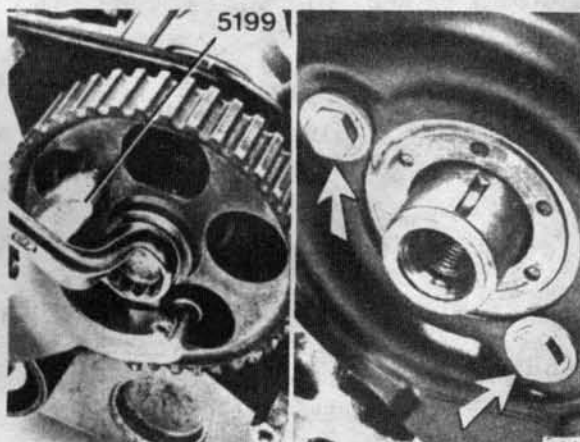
Снятие шестерни распредвала двигателя В172
